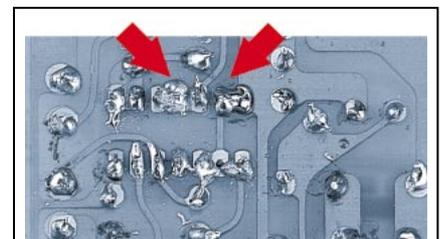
Après avoir soudé toutes les broches du support sur les pistes du circuit imprimé, nous vous conseillons de contrôler chaque soudure à la loupe car il peut arriver qu'une grosse goutte d'étain court-circuite deux pistes voisines.
